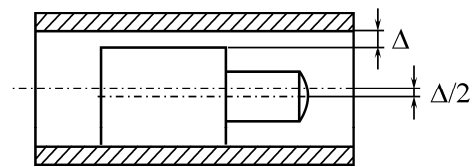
Параллельное смещение ударника в корпусе при горизонтальном положении пневмомолота: Δ — зазор по направляющей
